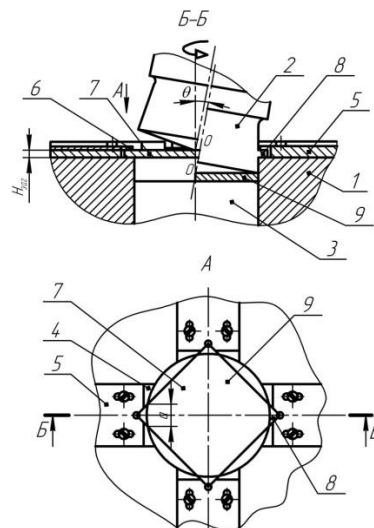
Схема виготовлення деталей штамповкою обкочуванням із квадратної заготовки
